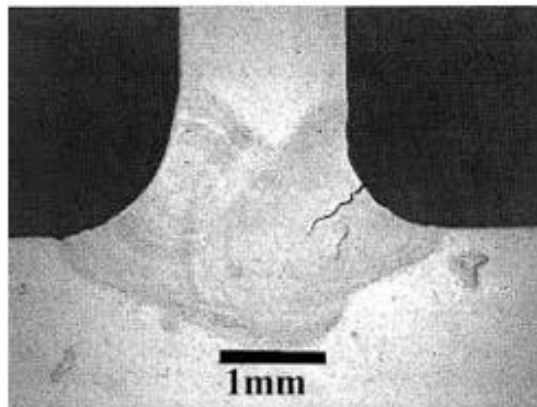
Fissuration d'une dent d'engrenage.[10]
